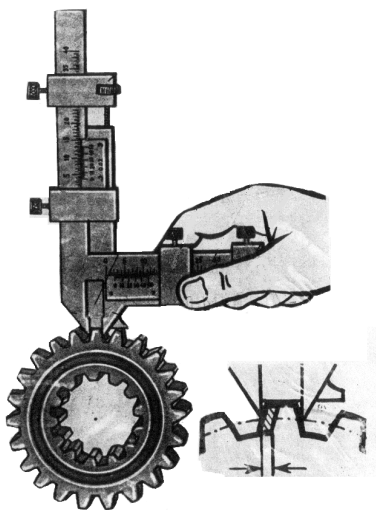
Схема измерения толщины зуба шестерни штангензубомером
